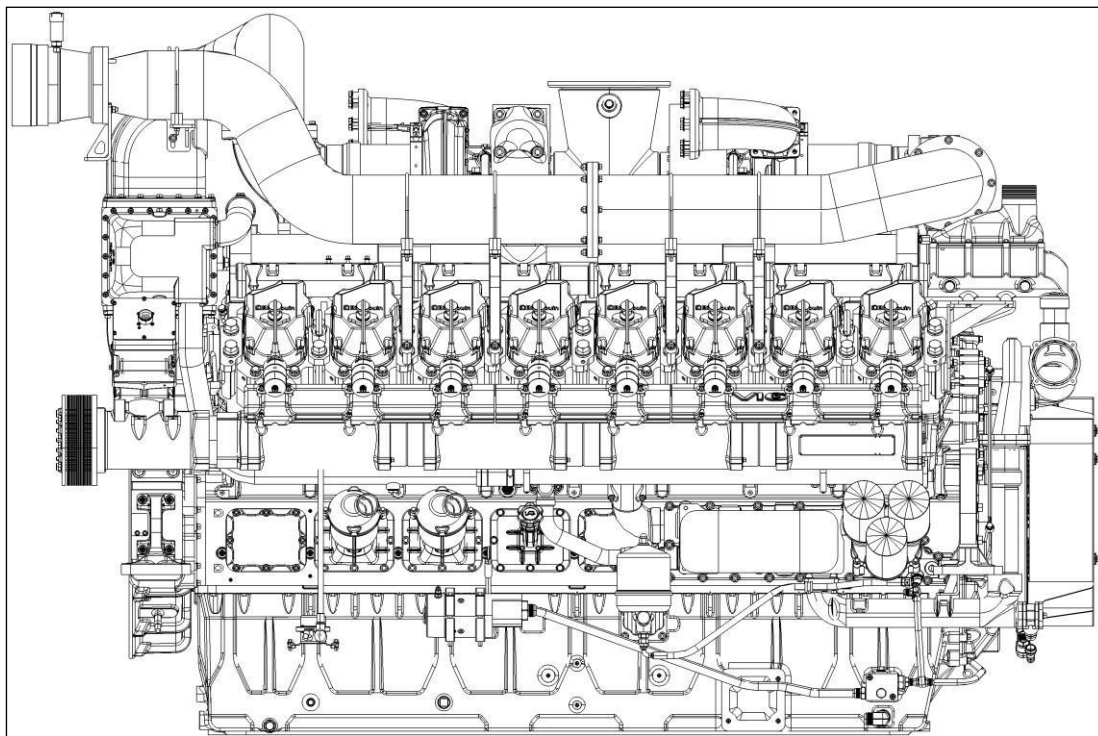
В – Внешний вид газопоршневого двигателя
